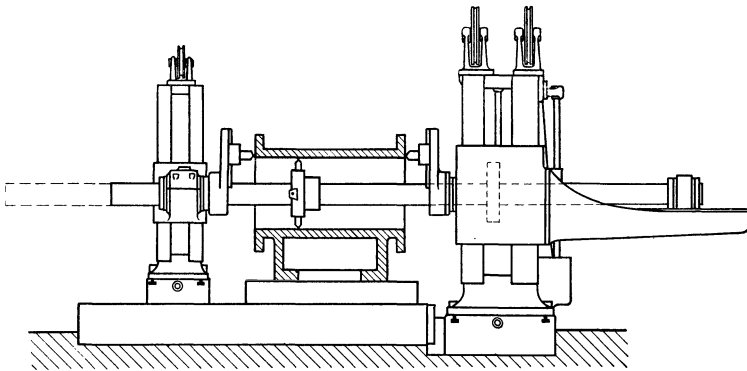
Ausbohrmaschine mit verschiebbarer Bohrstange und in der Höhe einstellbarem Spindelkasten.
